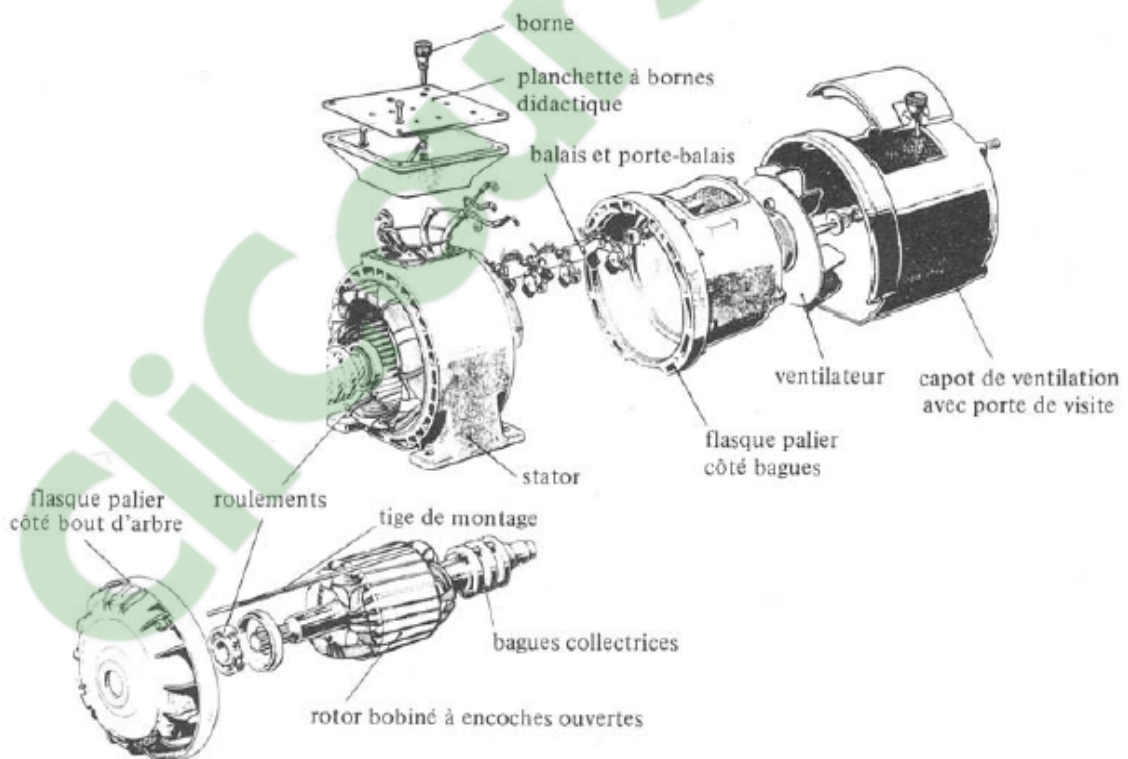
B : Vue éclatée d'une machine asynchrone triphasée à bagues.
